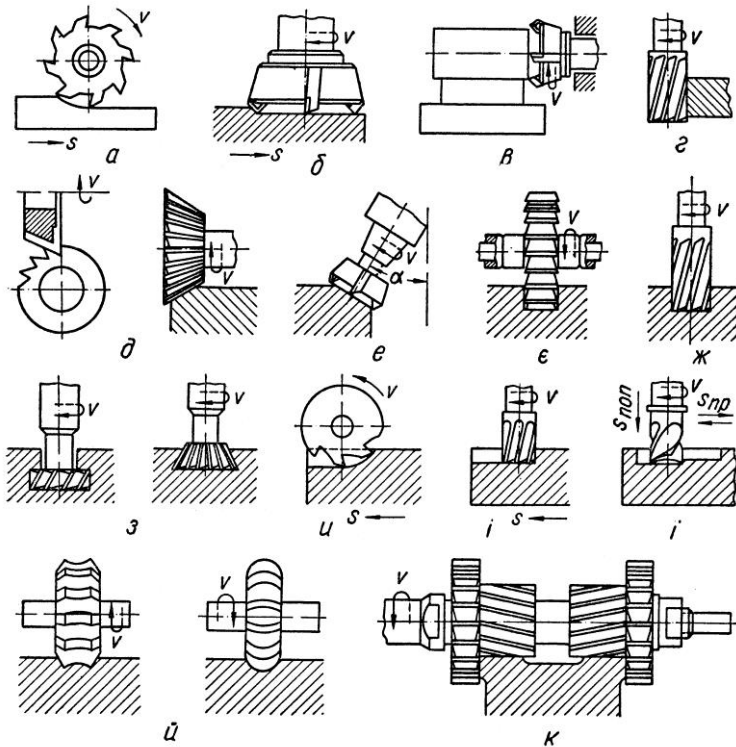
Приклади робіт, які виконуються на фрезерних верстатах:
